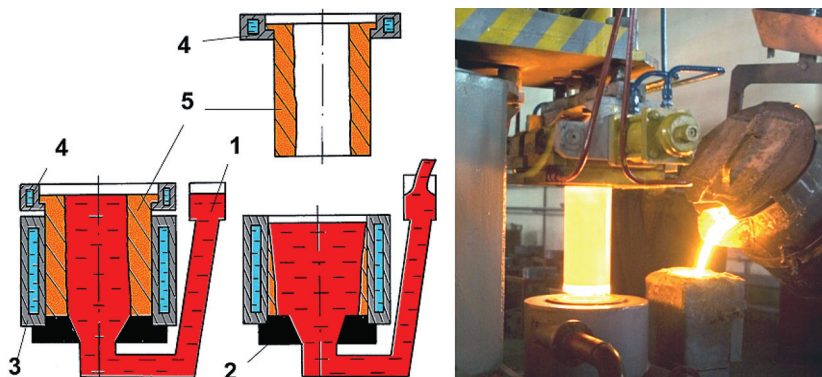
Принципиальная схема (а) и процесс (б) непрерывно-циклического литья полых заготовок без стержня: 1 – металлопровод; 2 – соединительный стакан; 3 – стационарная часть кристаллизатора; 4 – подвижная часть кристаллизатора (захваты); 5 – отливка
